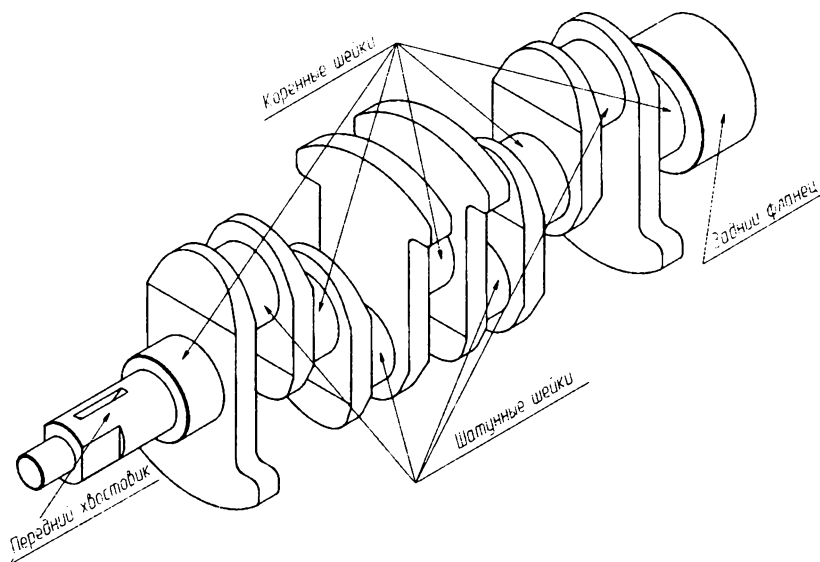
Основные конструктивные элементы коленчатого вала двигателя автомобиля ВАЗ
